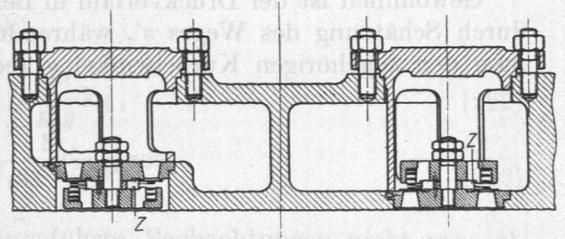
Kompressorsaug- und -druckventil (Deutsche Maschinenfabrik A.-G., Duisburg).
